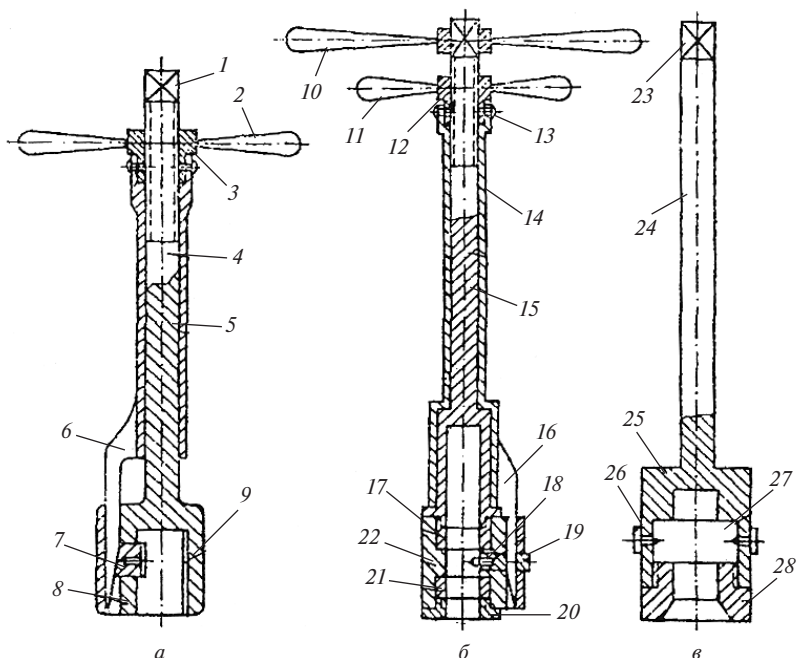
Набор инструментов для ремонта сифонных стояков с конденсаторными низкого давления:
